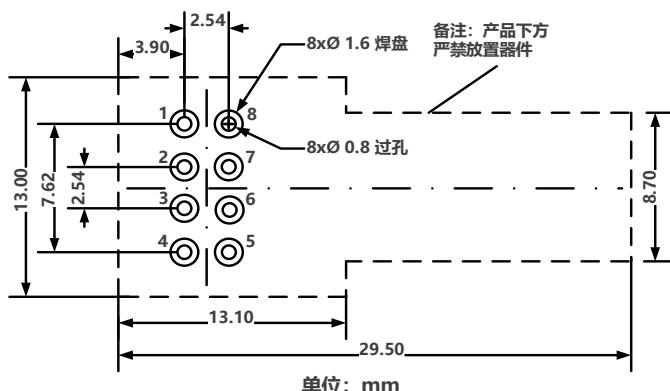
PCB Layout 设计推荐尺寸图 (俯视图)
